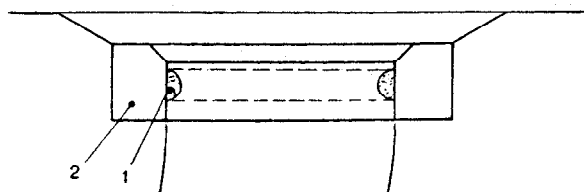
Extracción de un inserto de asiento de válvula con un cordón de soldadura de arco: 1 cordón de soldadura, 2 inserto.
